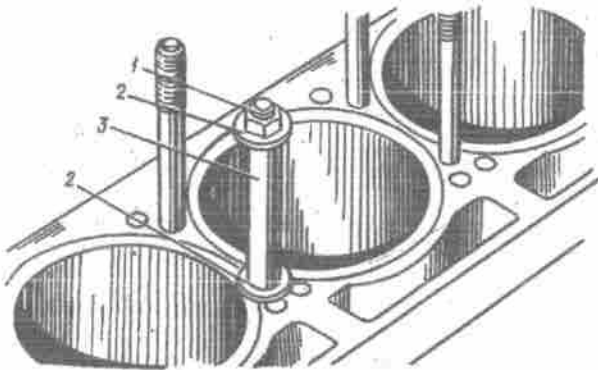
Andruckeinrichtung für die Laufbuchsen:
